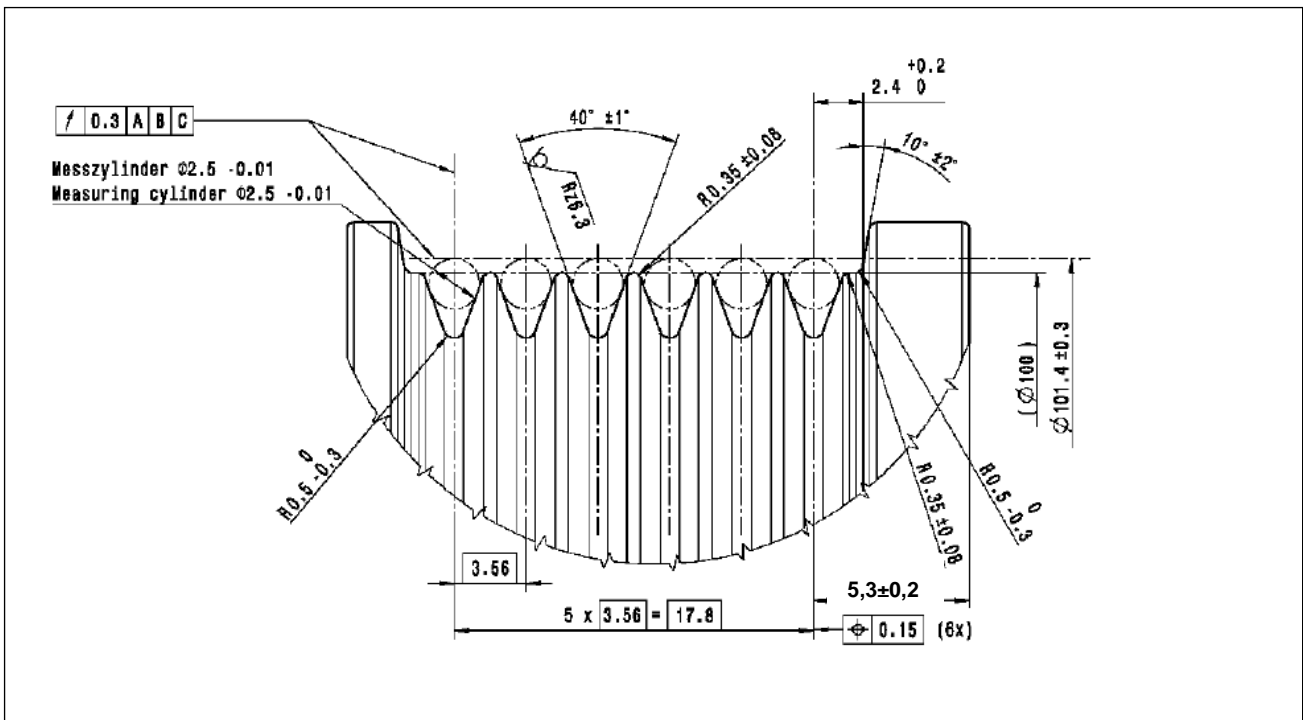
Деталь шкива привода компрессора климатической установки Denso 6SU14, диаметр шайбы d=100 мм
